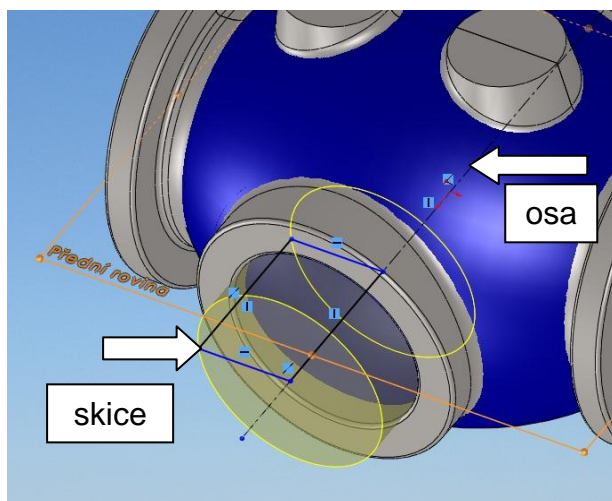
Zobrazený tvar rotace objemového tělesa příkazem Revolved
